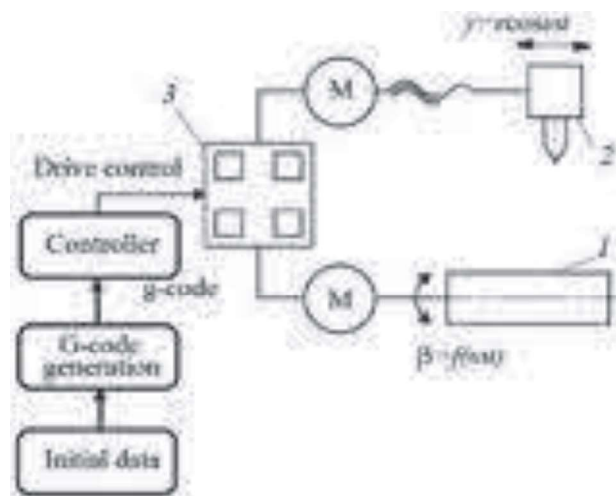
Схема управления процессом обработки отверстия: 1 заготовка; 2 резак; 3 плата с драйверами
